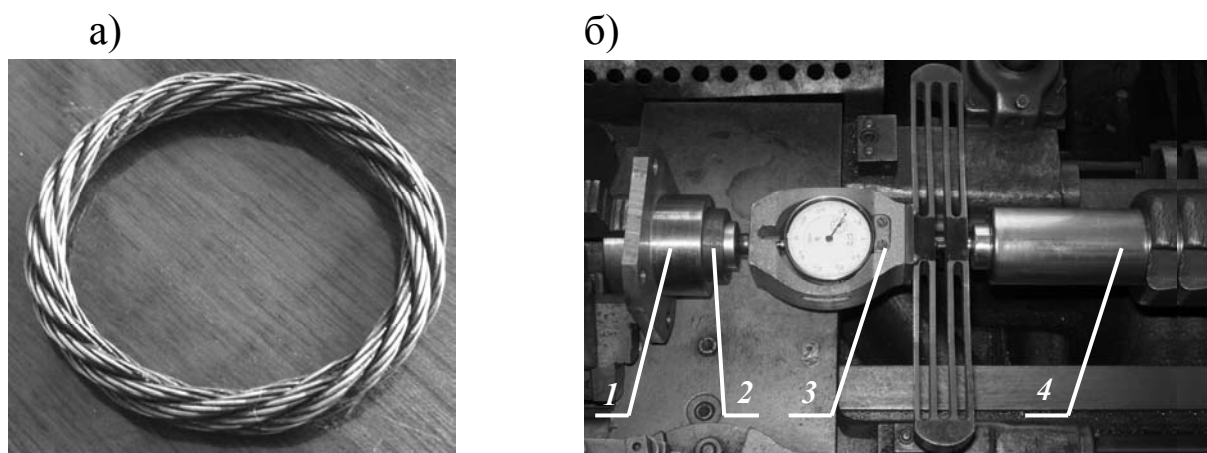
Внешний вид кольцевого канатного виброизолятора (а), установка для проведения статических испытаний (б)
